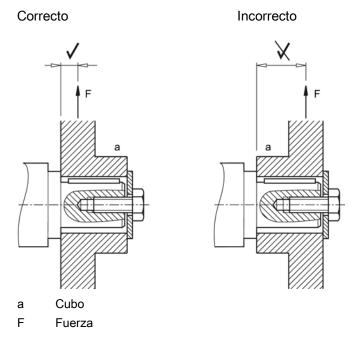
Disposición de montaje para reducir la carga sobre los ejes y rodamientos
